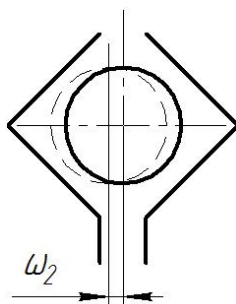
Похибка положення заготовки в захватному пристрої
